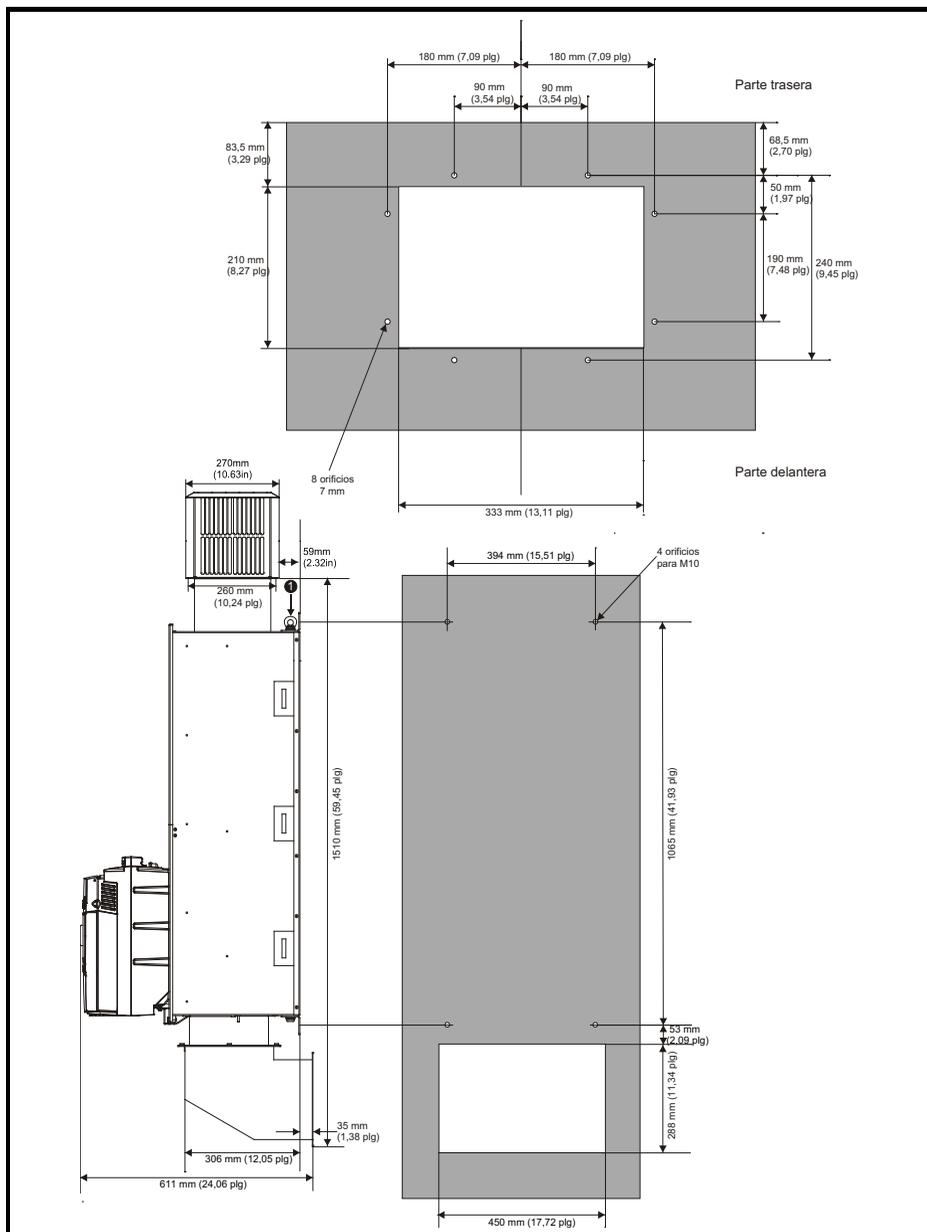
Placa posterior y detalles de montaje de los accionamientos de tamaño 2D
